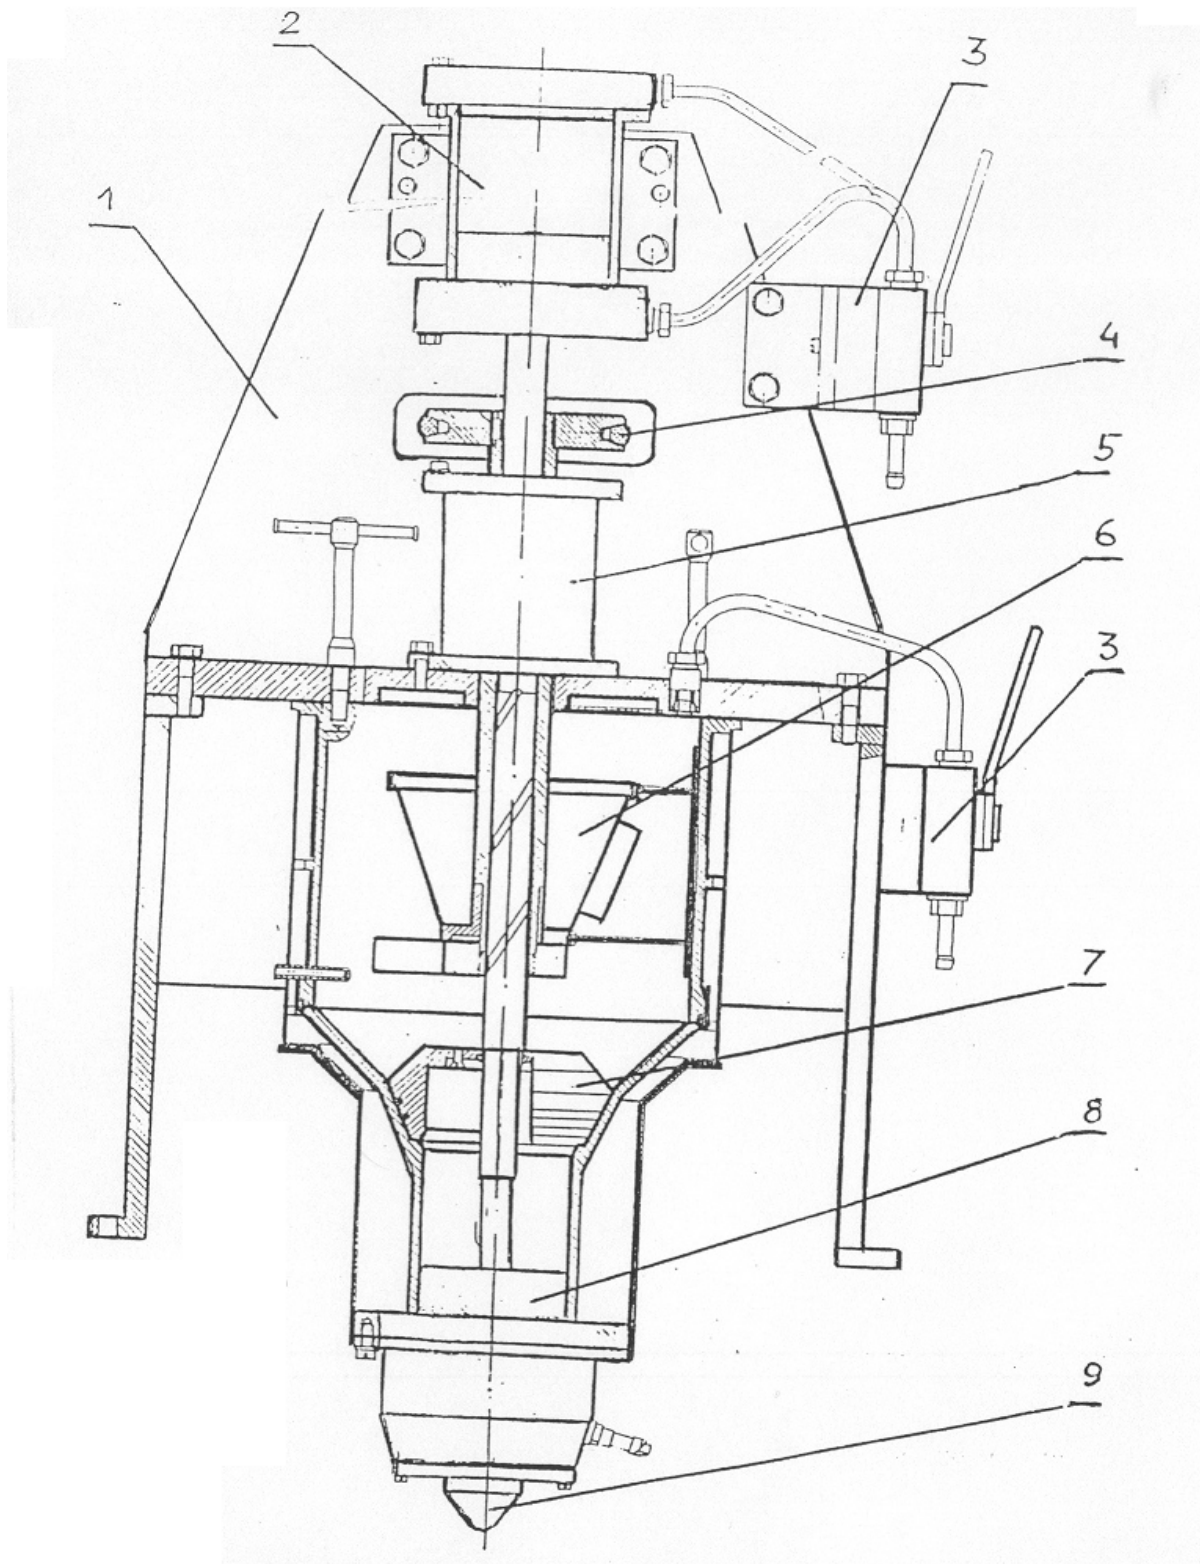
Быстроходный конусный смеситель периодического действия: 1 – станина; 2 – привод механизма запрессовки; 3 – распределители; 4 – приводной шкив; 5 – опорный узел; 6 – смеситель; 7 – поршень-разделитель; 8 – поршень для запрессовки модельного состава; 9 – клапан.
